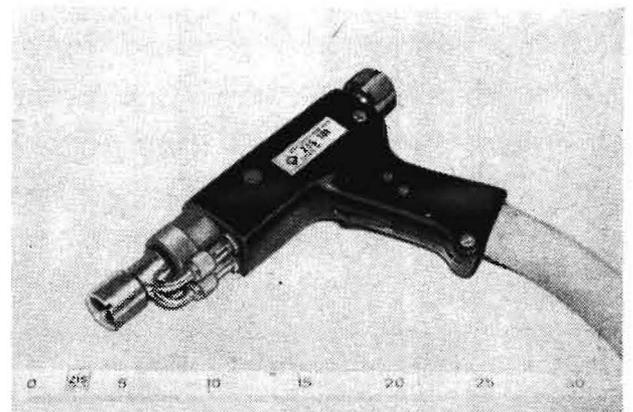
WIG-Schweißbrenner ZIS 290 und ZIS 224
